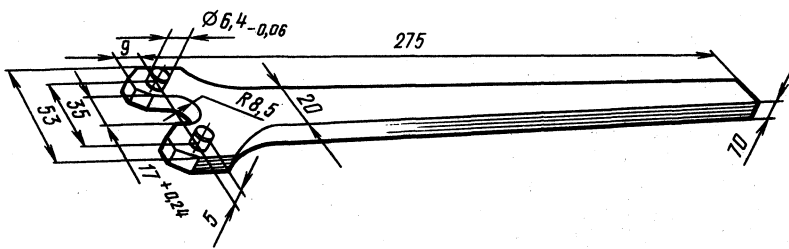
Ключ для резервуара амортизатора автомобиля «Москвич-412»
